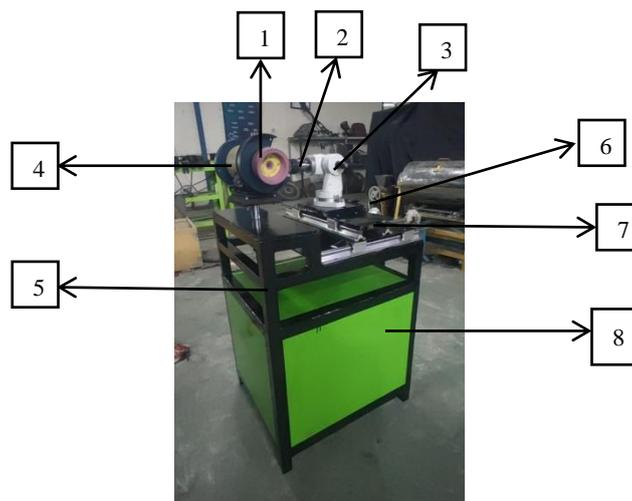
Desain Mesin *Tool Grinding Endmill
